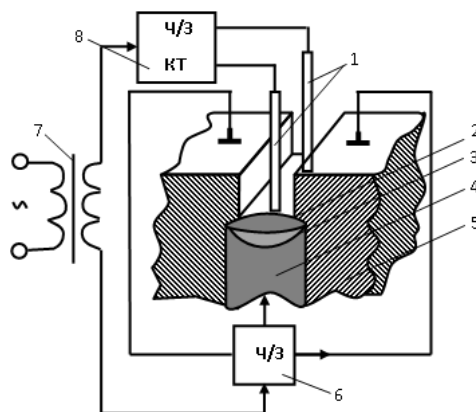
Схема ЭШС с коммутацией токоподводов: 1 — электроды; 2 — шлаковая ванна; 3 — металлическая ванна; 4 — сварной шов; 5 — изделие; 6 — трехканальный преобразователь тока; 7 — источник питания; 8 — двухканальный коммутатор тока
